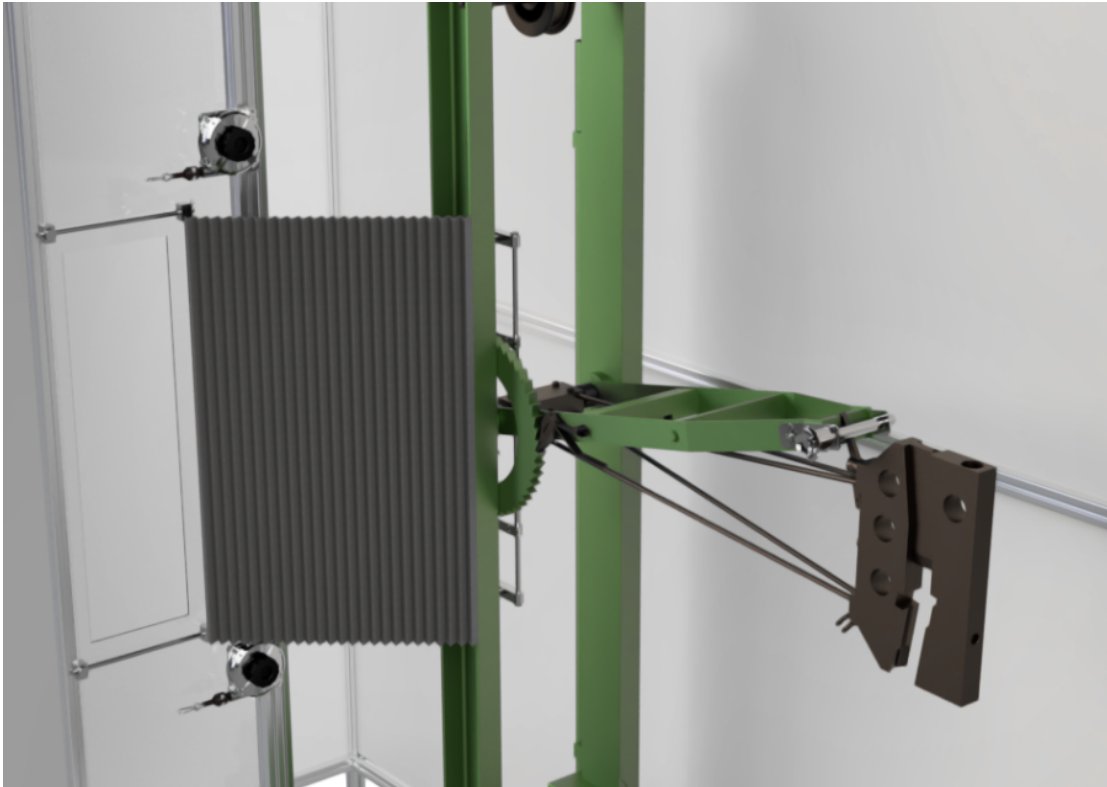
Soffietto piano e Spina di bloccaggio rapida
